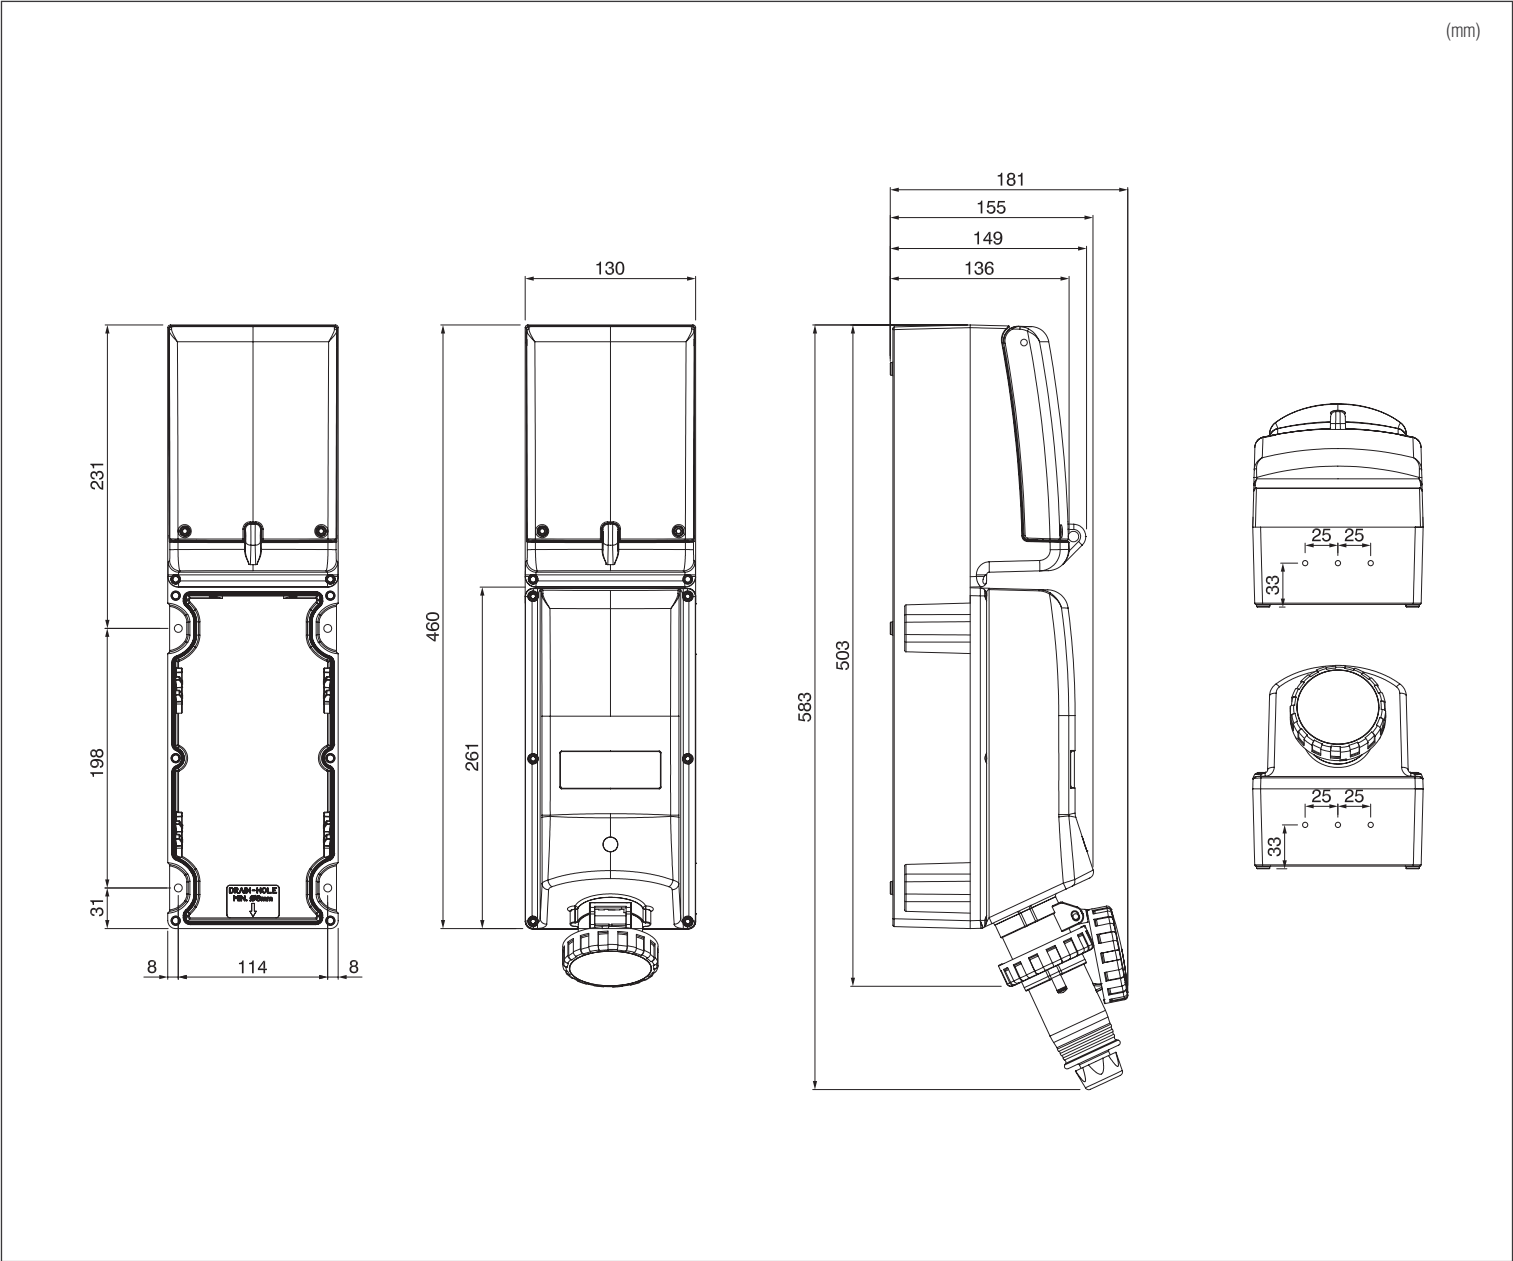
IT: Disegno tecnico della presa interbloccata EN: Technical drawing of the interlocked socket FR: Schéma technique de la prise interverrouillée ES: Diseño técnico de la toma con enclavamiento
